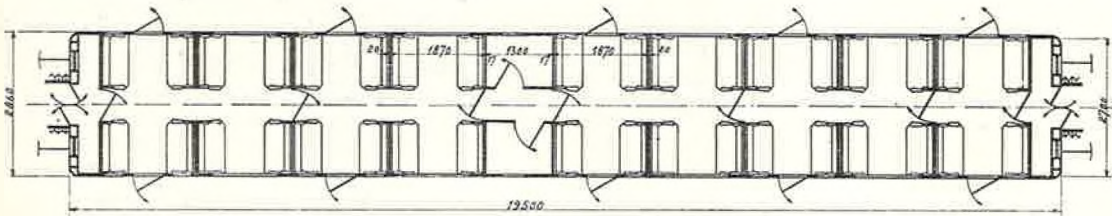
Coupérijtuig 3e klasse met doorgang en vouwbalgen. (Nord Français).
